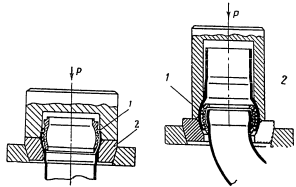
Обкатка шаровых обойм патрубков выхлопного коллектора.
